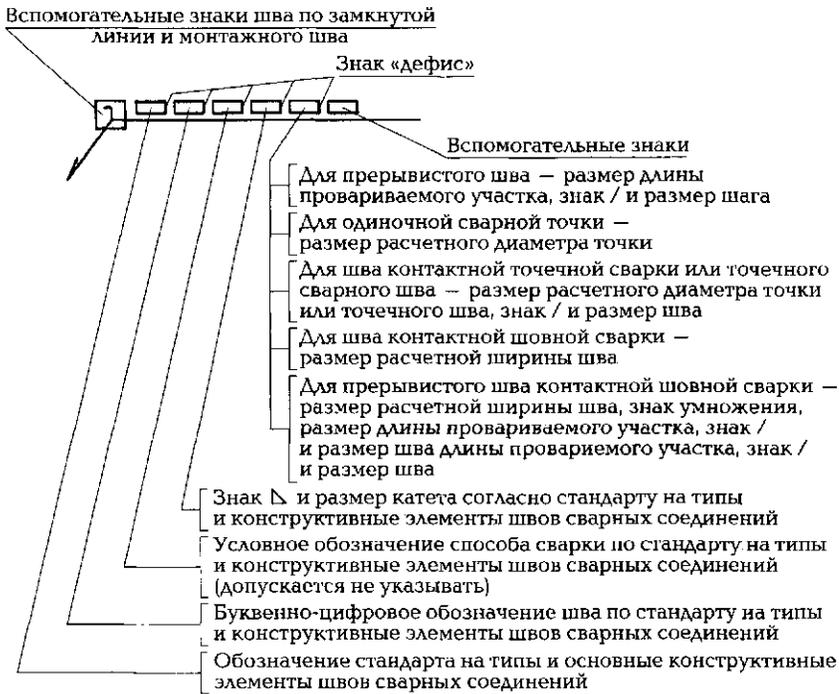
Структура условного обозначения стандартного шва или стандартной одиночной сварной точки
